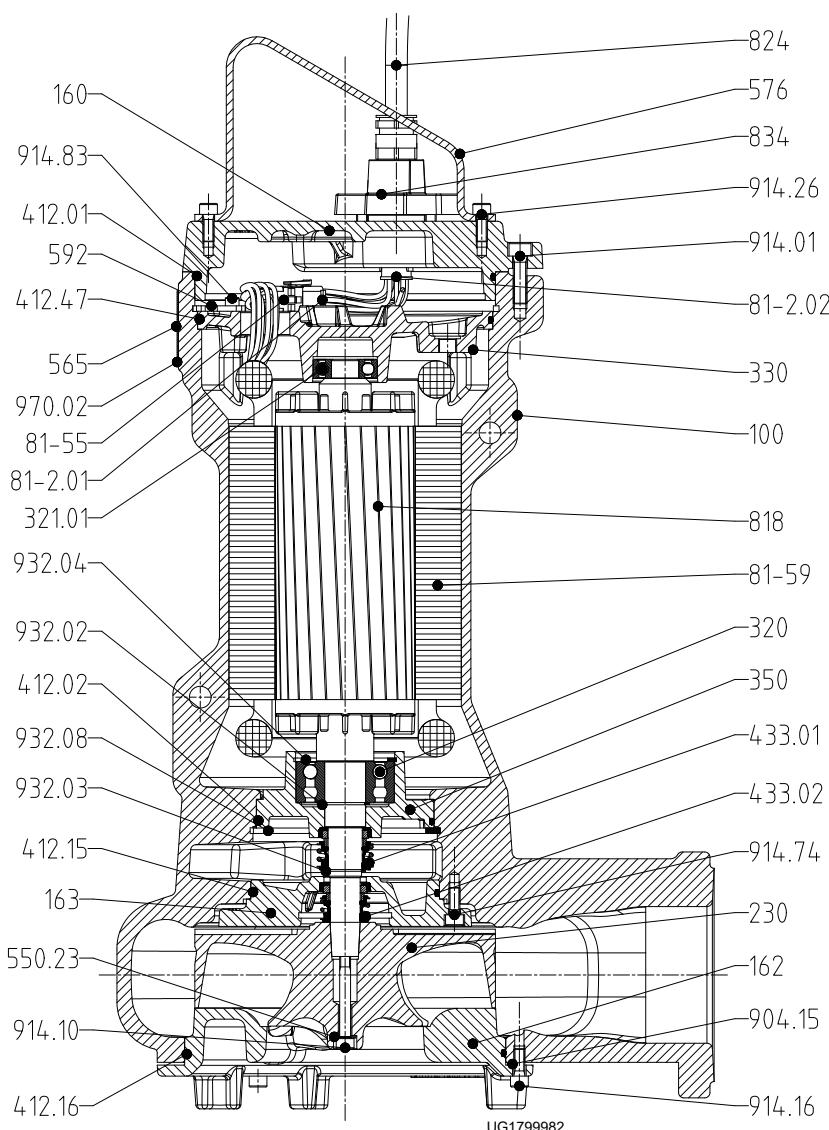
Сборочный чертеж для исполнения YS, рабочее колесо D-max
